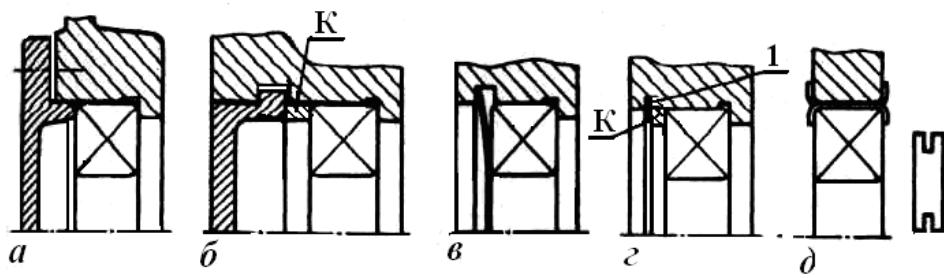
Способы крепления подшипников в корпусе: 1 – пружинное кольцо, К – компенсаторное кольцо
